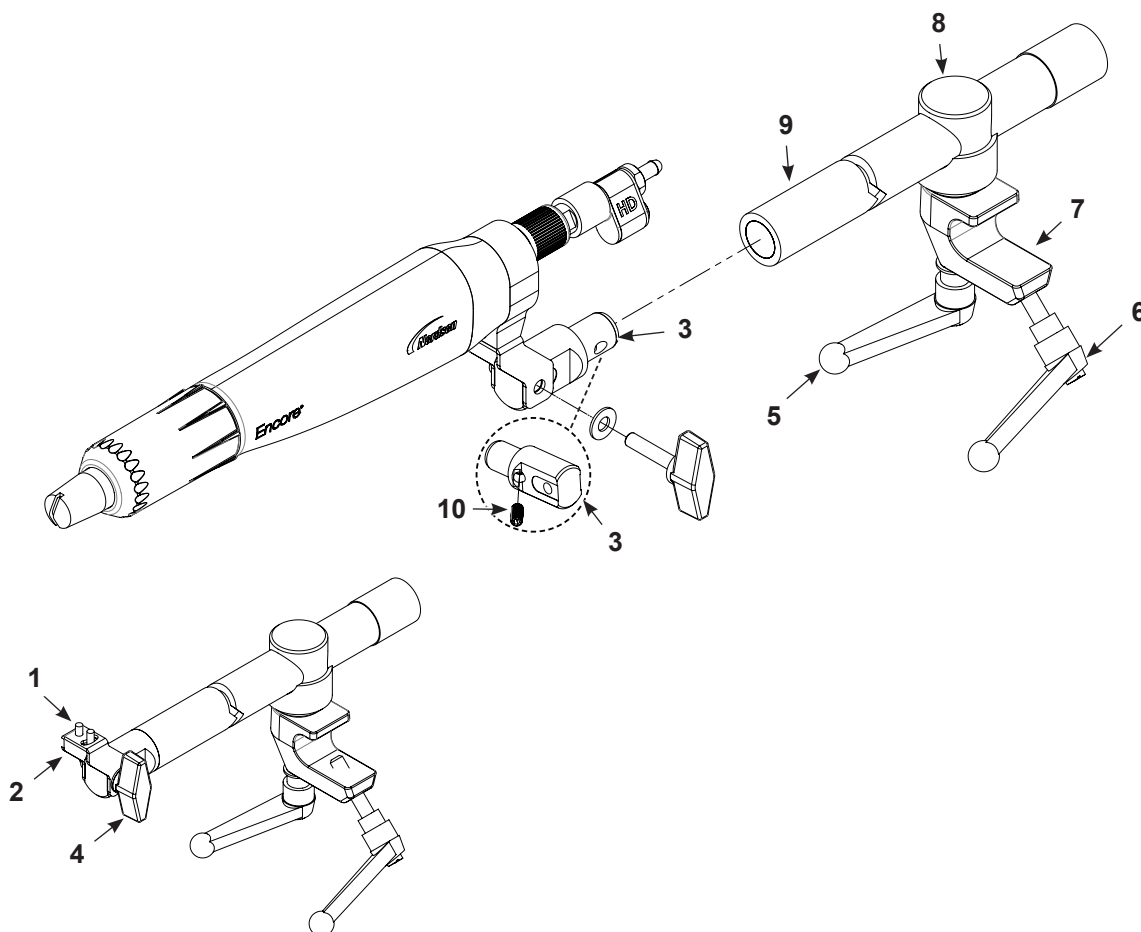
Fixation d'un pistolet de pulvérisation à fixation sur barre
